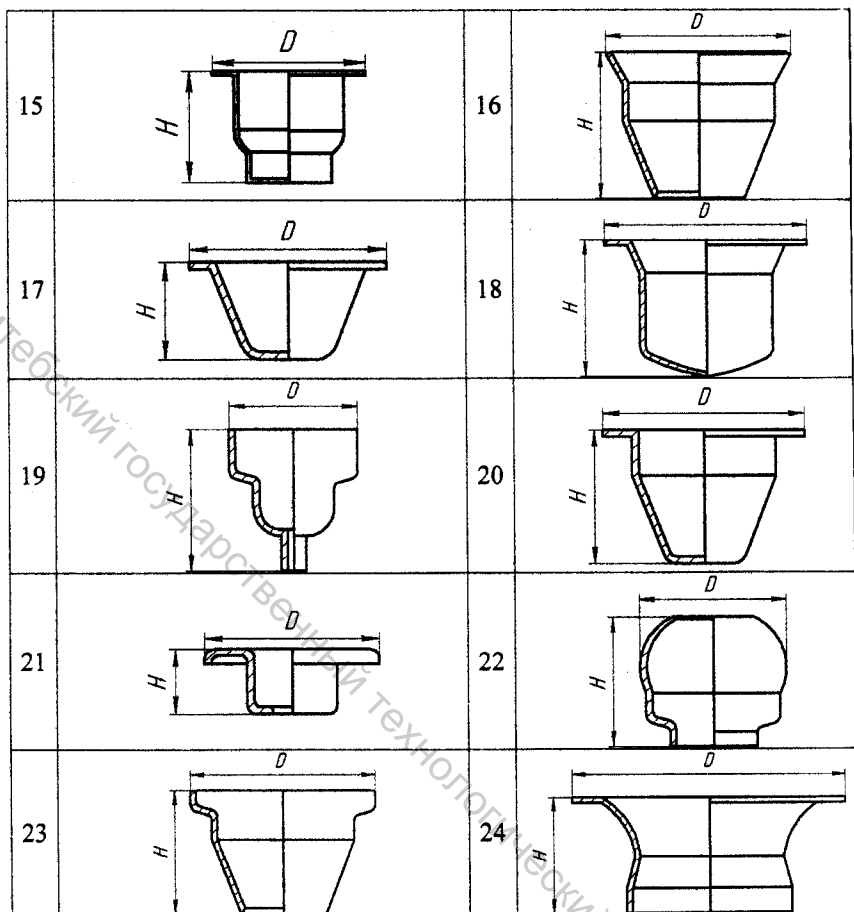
Схема простановки размеров заготовки, получаемой вытяжкой
